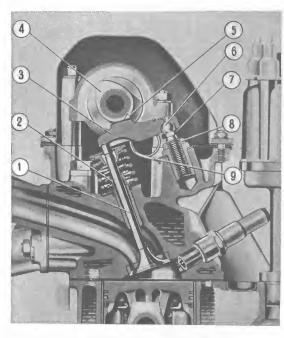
Клапанный механизм: 1 — клапан; 2 — защитный колпачок; 3 — рокер; 4 — распределительный вал; 5 зазор между ропером и кулачком; 6 сферическая головка регулировочного болта; 7 — шестигранник регулировочного болта; 8 — контргайка; 9 — шпилечная пружина рокера.
